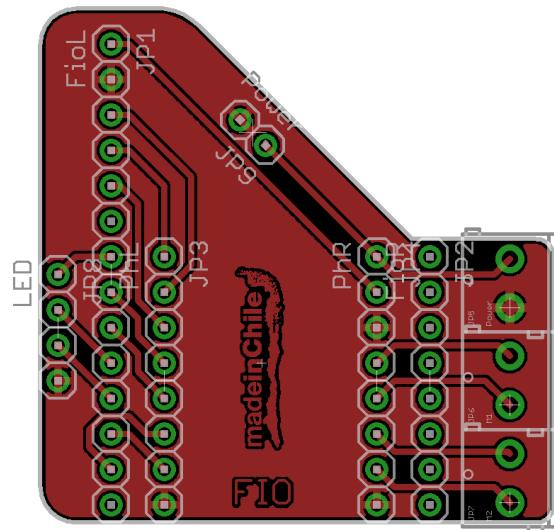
MODIBoard es una PCB diseñada para poder conectar de forma simple los diversos componentes electrónicos. Conecta: Arduino Fio, Lipo Rider Pro, Motor Driver, LED RGB y Motores.
